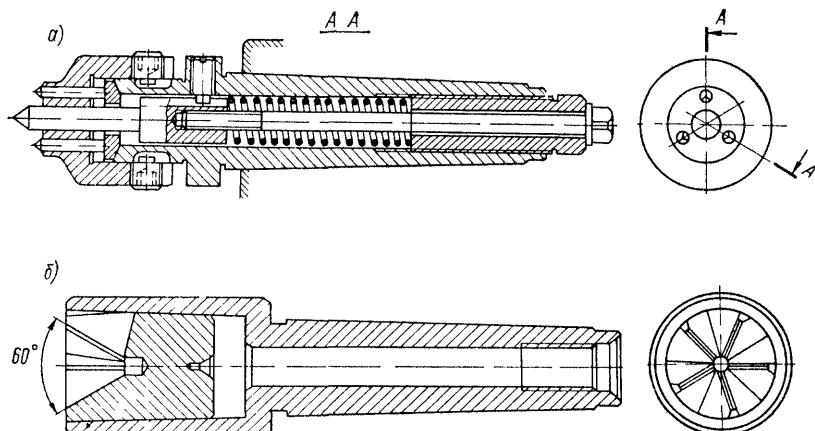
Поводковый токарный патрон с базированием заготовок на центр и передачей крутящего момента торцевыми зубьями (а) и поводковый токарный патрон с базированием заготовок на внутренний конус патрона и передачей крутящего момента внутренними зубьями (б)
